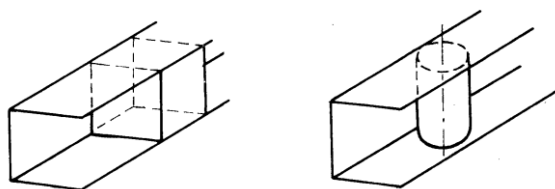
Příklady integrálních stěn vytvořených odleptáním [9].
